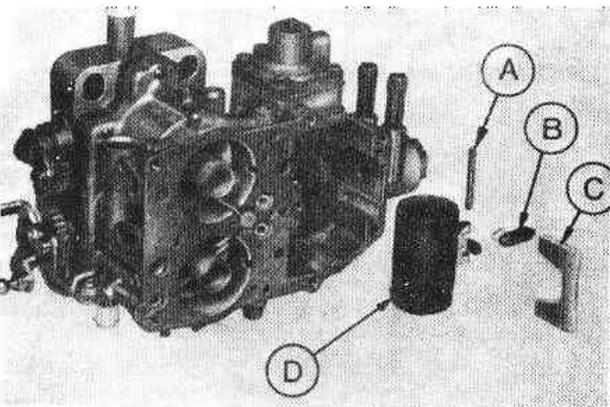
Установка игольчатого клапана и поплавка в сборе (Разд.34) А. Штифт В. Игольчатый клапан
